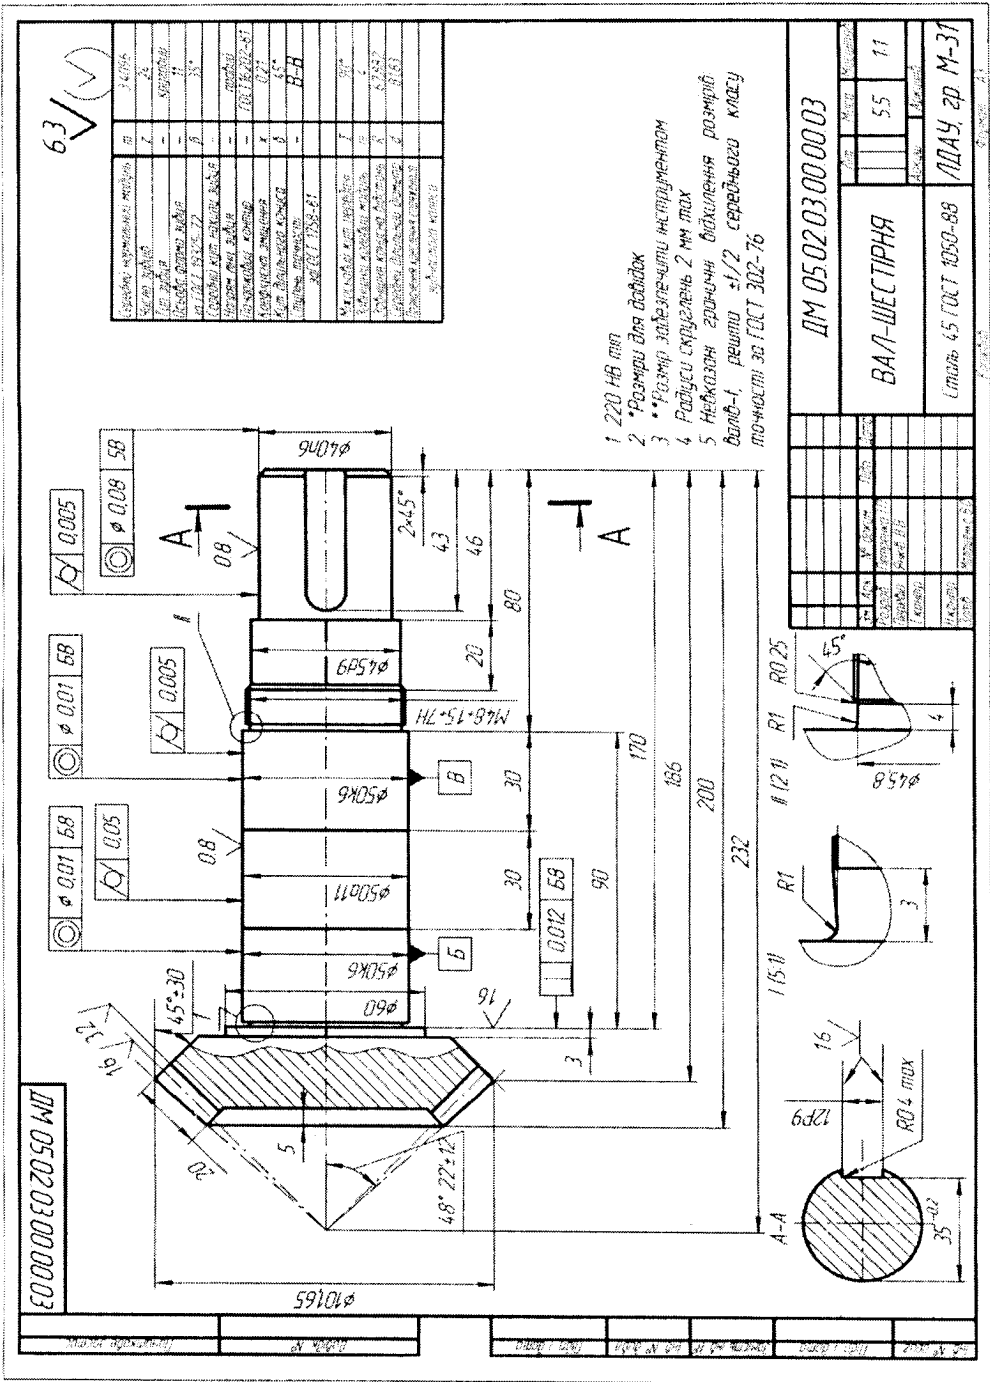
Приклад робочого креслення вала-шестерні конічної
